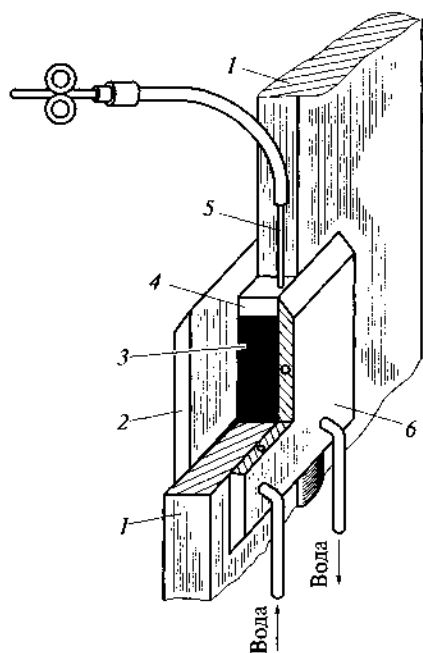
Схема электрошлаковой сварки:
